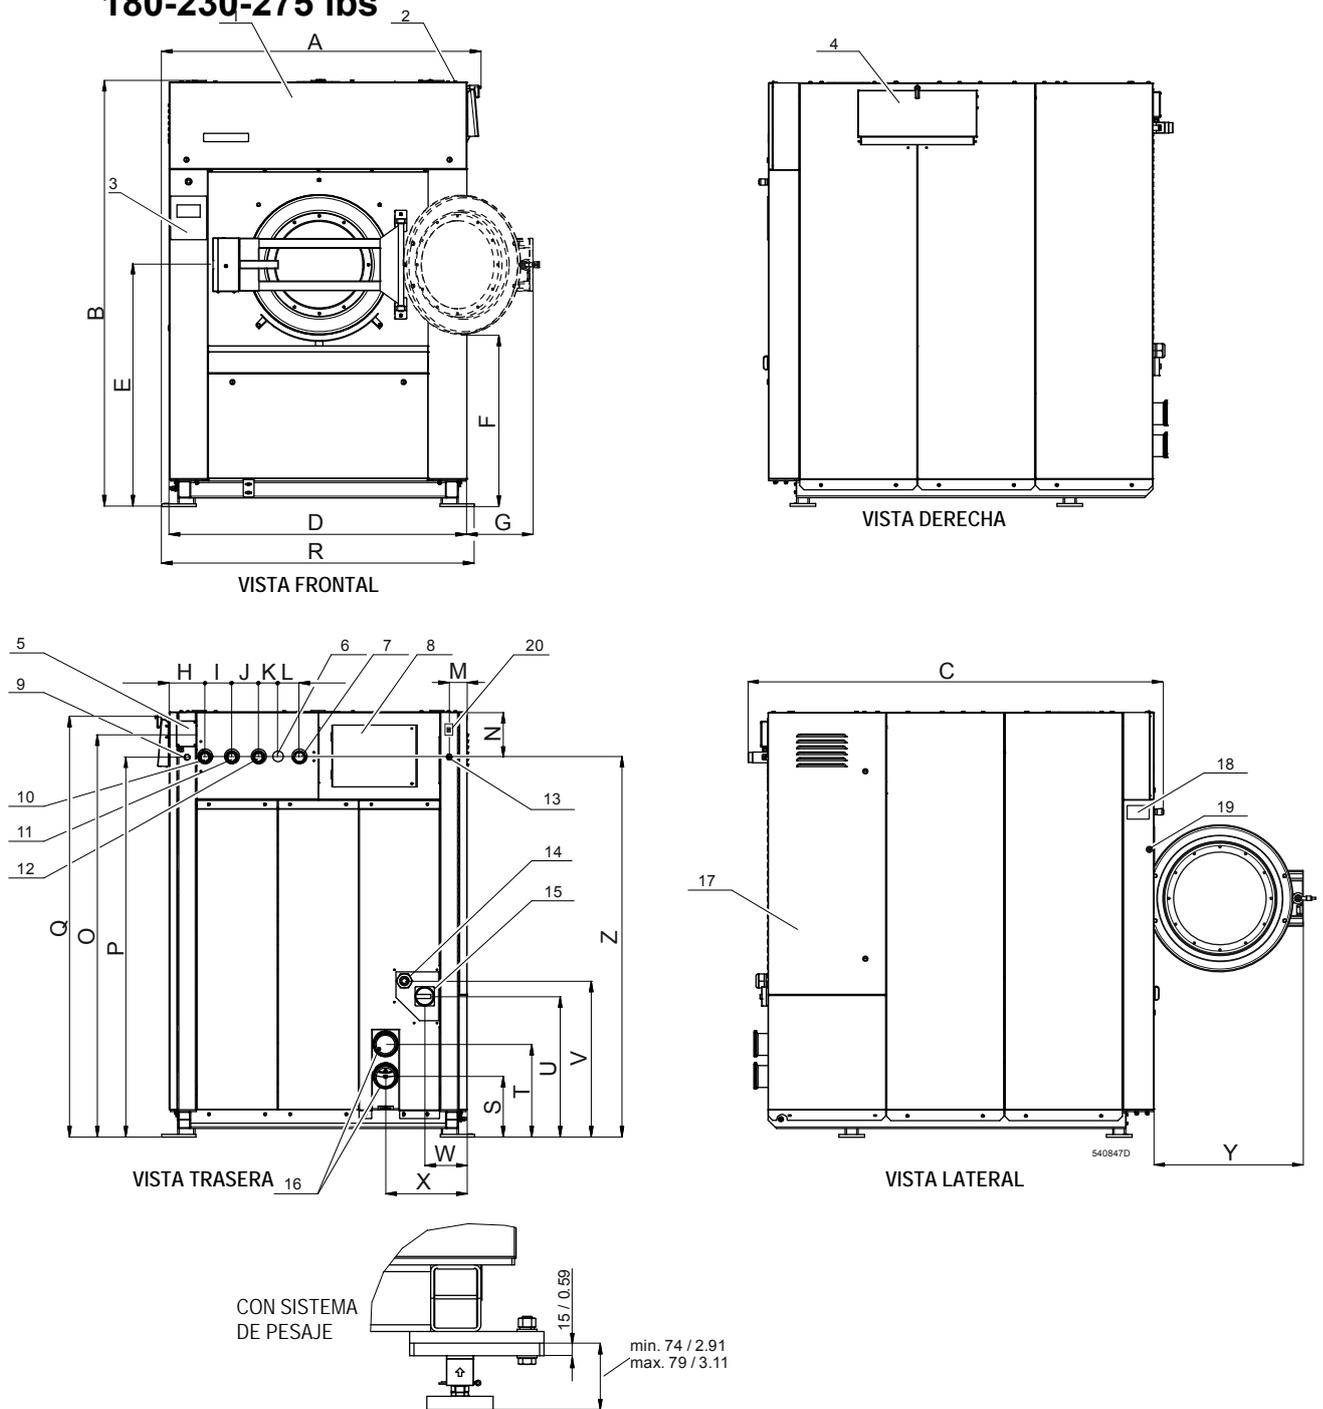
Máquinas 80-100-120 kg / 180-230-275 lbs, (dimensiones en mm / pulgada)
